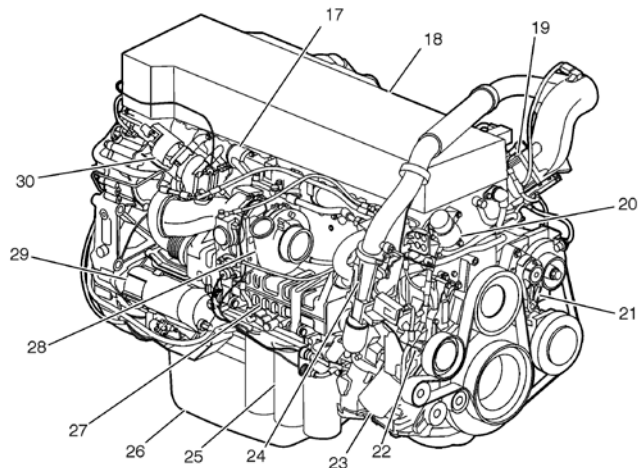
VUE D'ENSEMBLE DU MOTEUR D13H, CÔTÉ TURBOPRESSEUR
